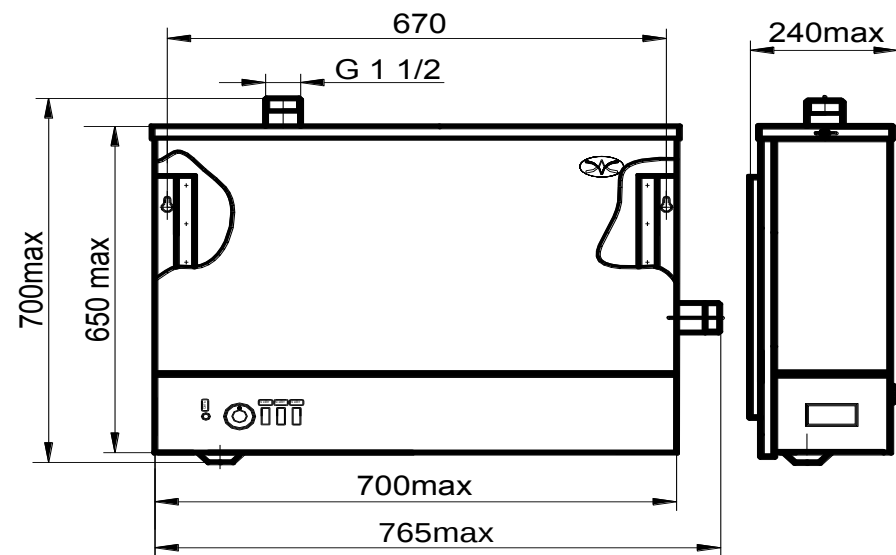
Водонагреватель ЭВПМ-36...48. Габаритный чертеж.
